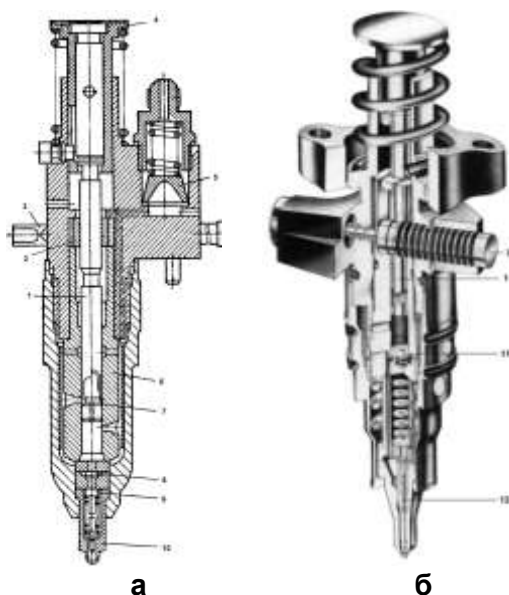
Механические насос-форсунки: а - Ленкарз; б - Steyr: 1 - плунжер; 2 - механизм поворота; 3 - рейка; 4 - толкатель; 5 - фильтры; 6 - втулка плунжера; 7 - управляющая кромка; 8 - клапан давления; 9 - обратный клапан; 10 - распылитель; 11 – клапан управления гидродогрузением иглы; 12 – игла.
